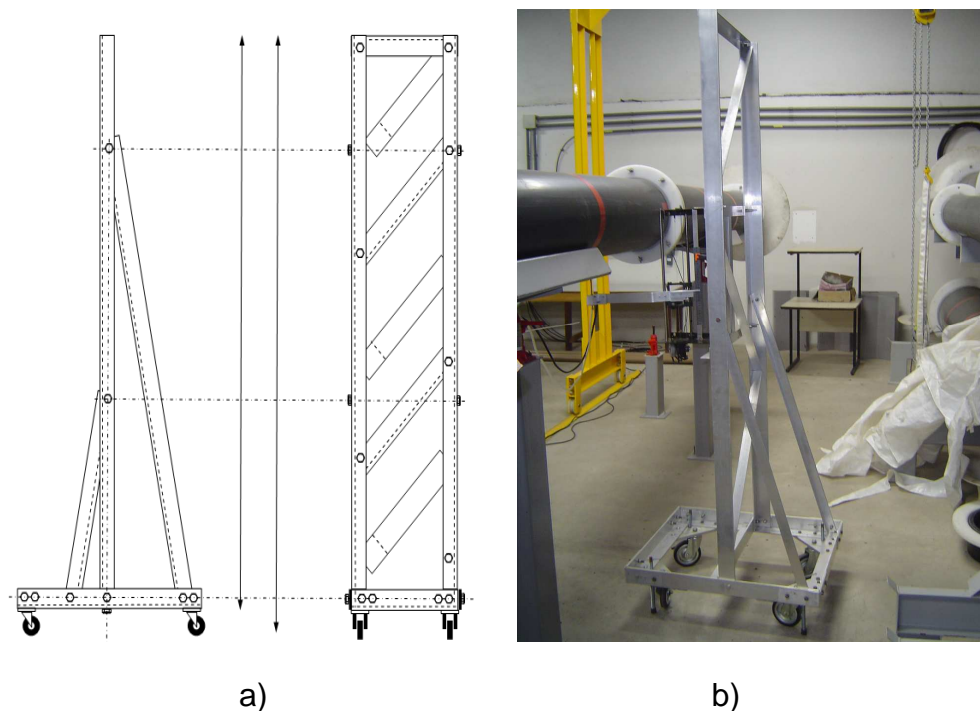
Carro de fixação utilizado no laboratório no passado[19] : a) croqui com vistas frontal e lateral; b) vista da montagem em operação.
